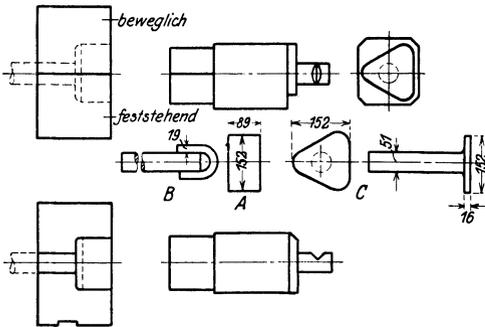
Schweißen und Stauchen einer Trittstange.
